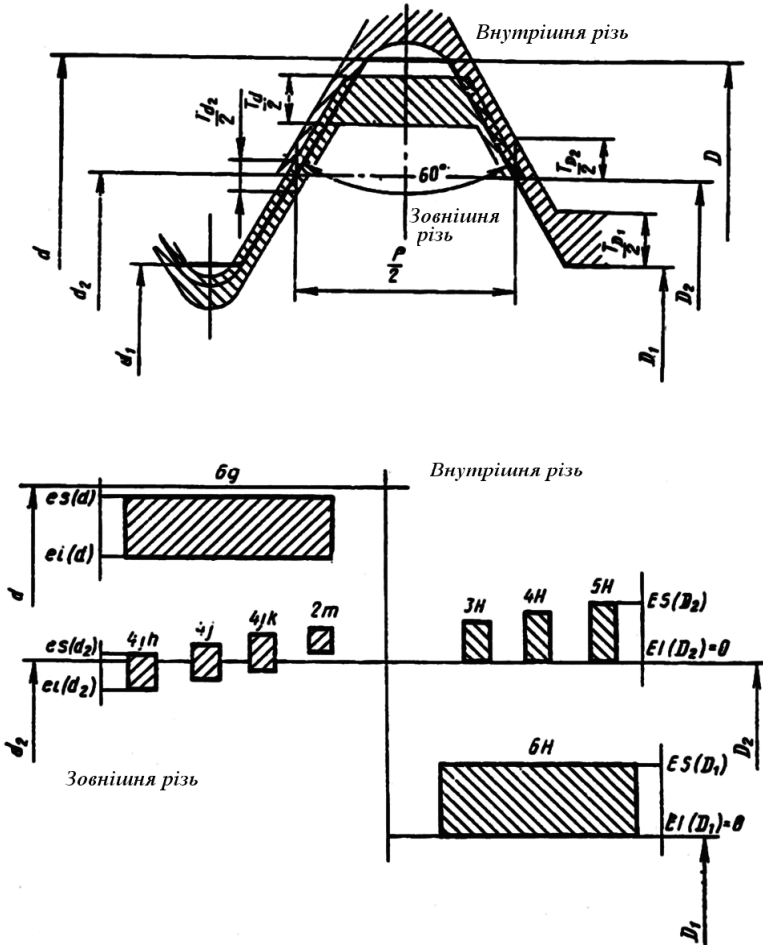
Розташування полів допусків перехідних різьблених з'єднань
